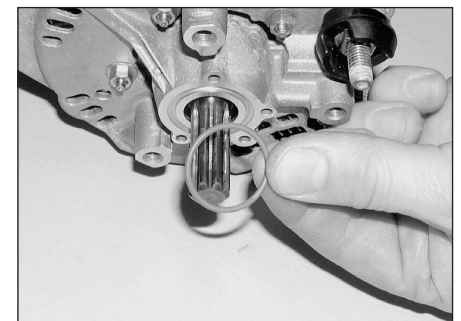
Замените уплотнительное кольцо на корпусе генератора – двигателя 1.7 л
